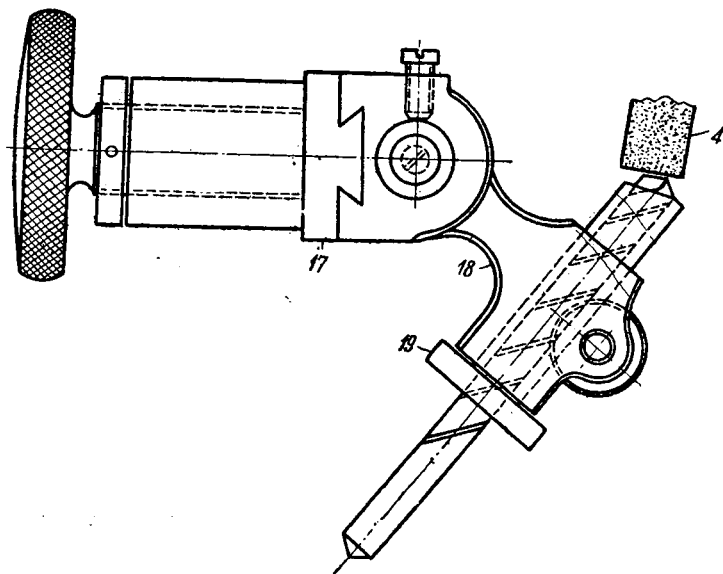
Приспособление для закрепления сверла станка Шток, тип ВN-I.
